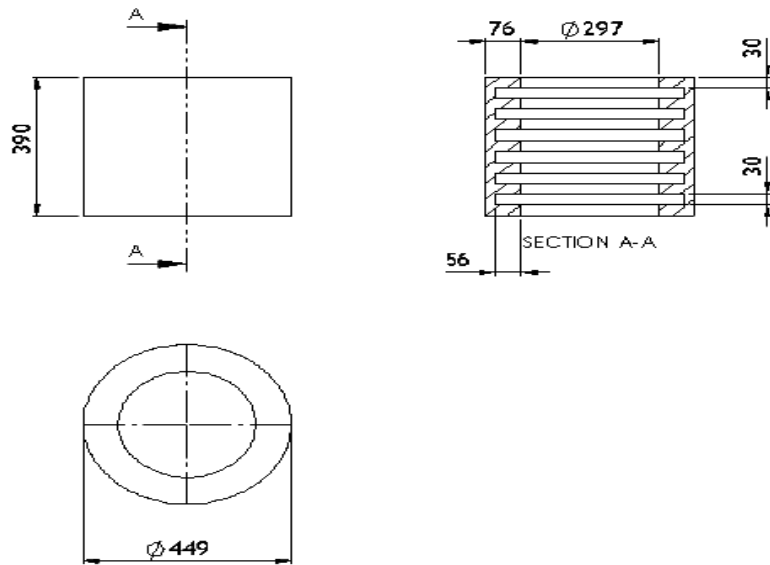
Dimensões finais do primário (mm) do gerador linear tubular [21]
